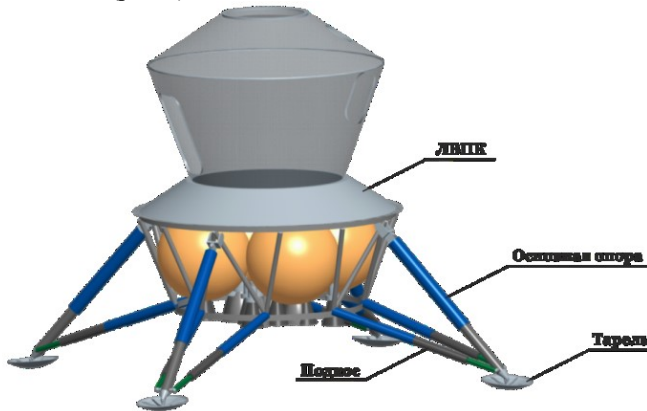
ЛВПК и конструкция опоры его посадочного устройства
